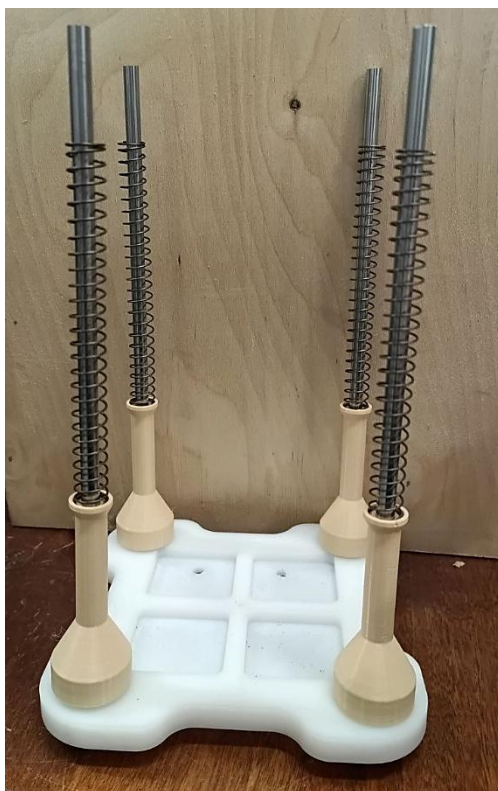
Неподвижная пластина с направляющими и возвратными пружинами
